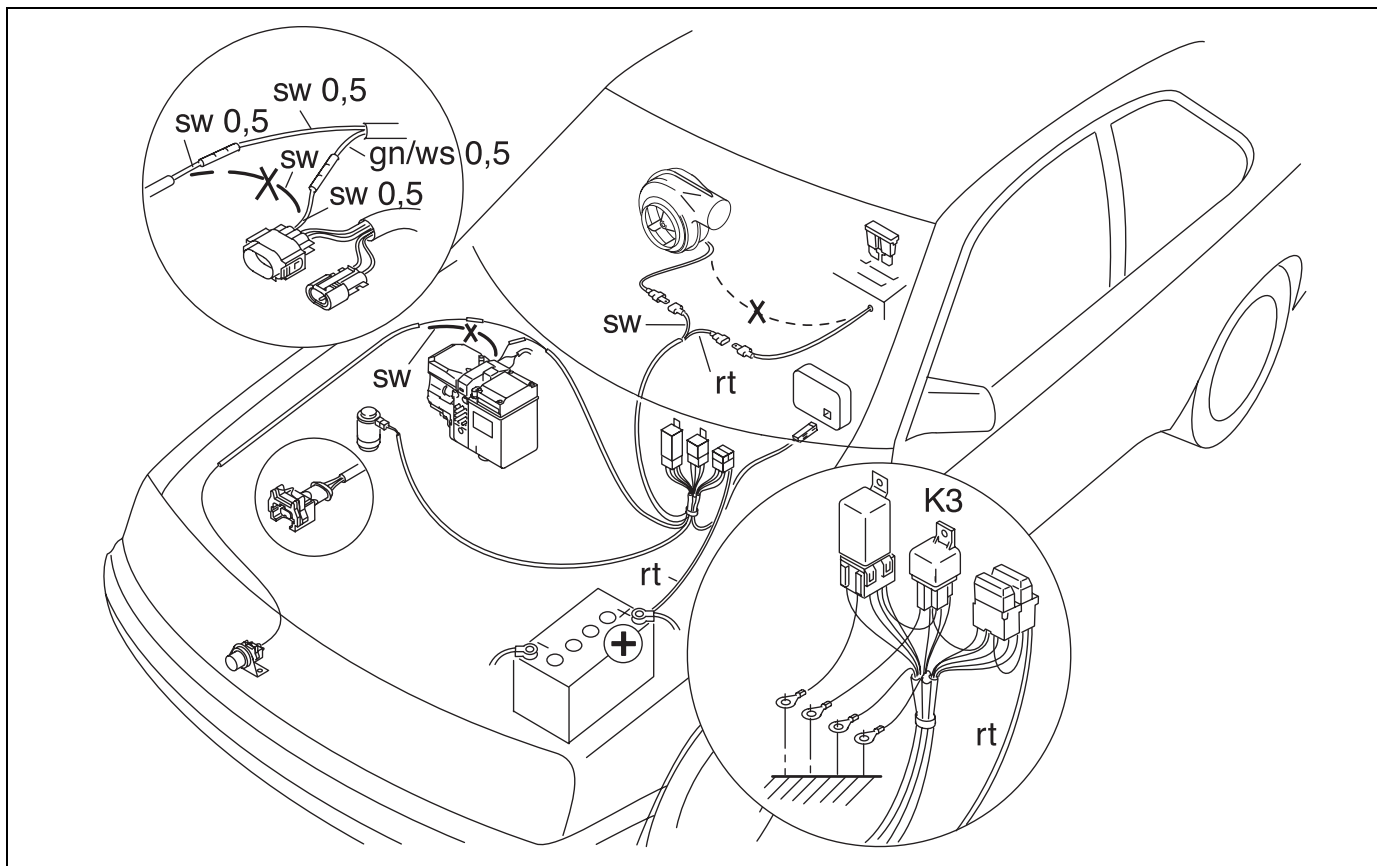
Postmontaggio Thermo Top Z su riscaldatore supplementare a vettura ferma
